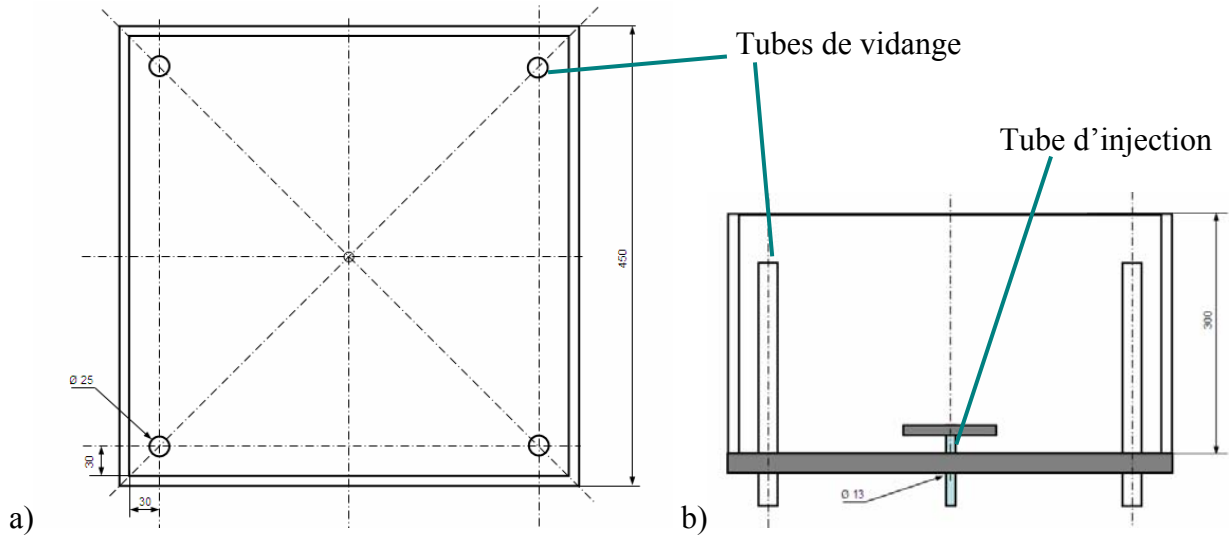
Plan de la cavité : a. vue de dessus; b. vue de face
